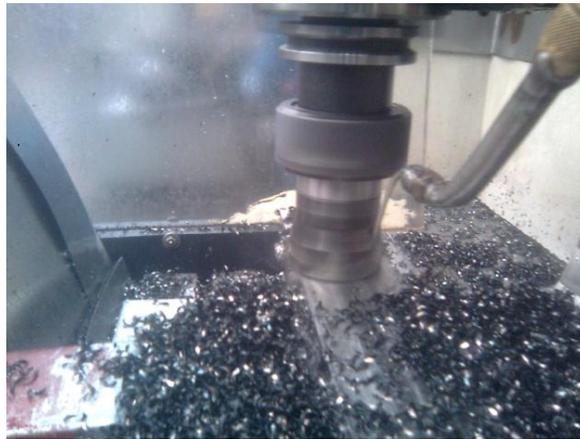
Fresado de la base del dispositivo marcador de probetas
